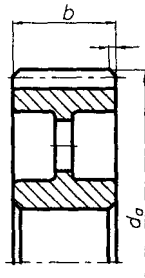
Основные размеры на чертеже цилиндрического зубчатого колеса
